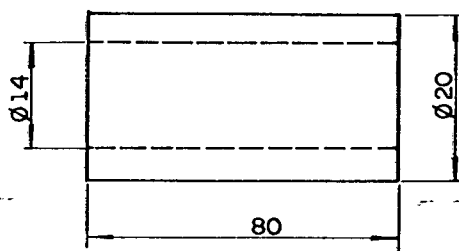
Dimensões do corpo de prova utilizado nos ensaios de torneamento longitudinal.
